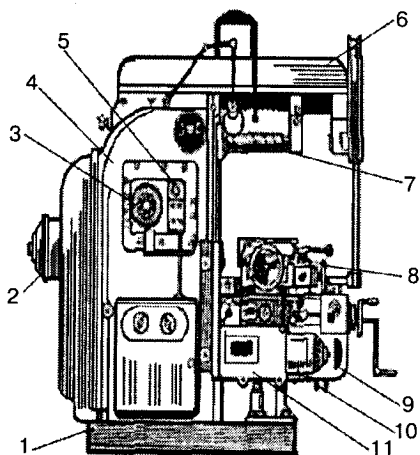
Консольно-фрезерний верстат 6М82Г:
